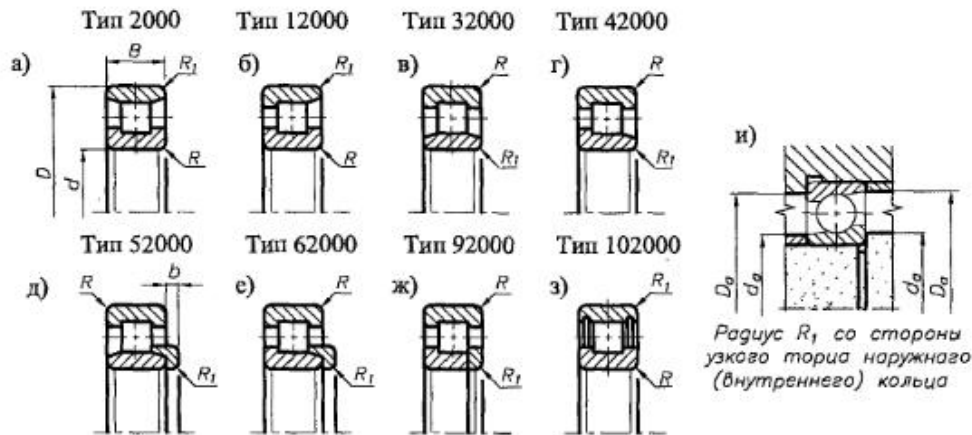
Габаритные и установочные размеры роликовых радиальных с короткими цилиндрическими роликами подшипников
